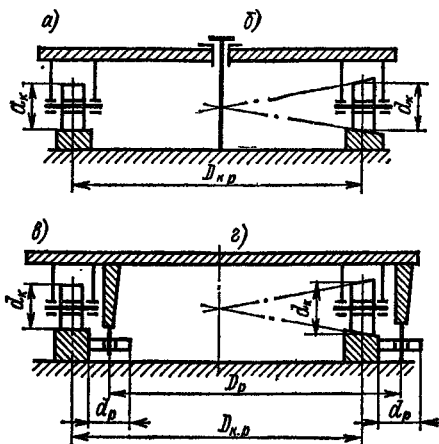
Опорно-поворотные устройства кранов (тележек) с круговым плоским или коническим рельсом и колесами (а, в — цилиндрическими; б, г — коническими) с центрирующей цапфой (а, б) и горизонтальными роликами (в, г)
